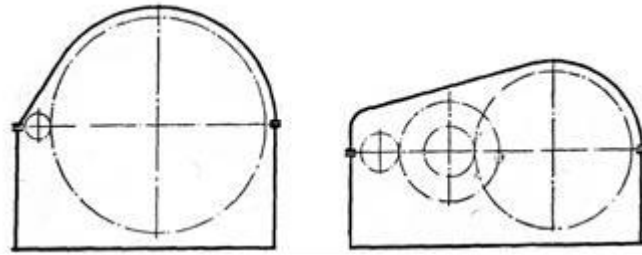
Зіставлення габаритів одноступінчастого і двоступеневого редукторів з циліндричними колесами при однаковому передавальному числі
